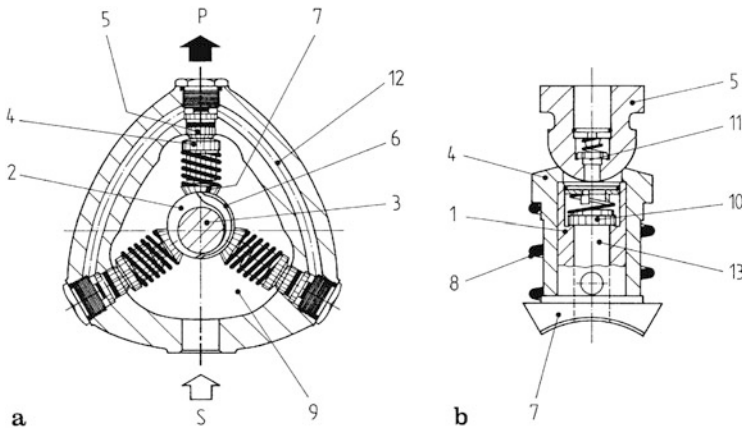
Radialkolbenpumpe, außen beaufschlagt (R4, Bosch Rexroth). a Querschnitt mit 3 über Gehäusekanäle zu einem Druckanschluss zusammengefassten Kolben; b Einzelelementpaarung Kolben/Zylinder mit Gleitschuh und sphärischem Stützelement
